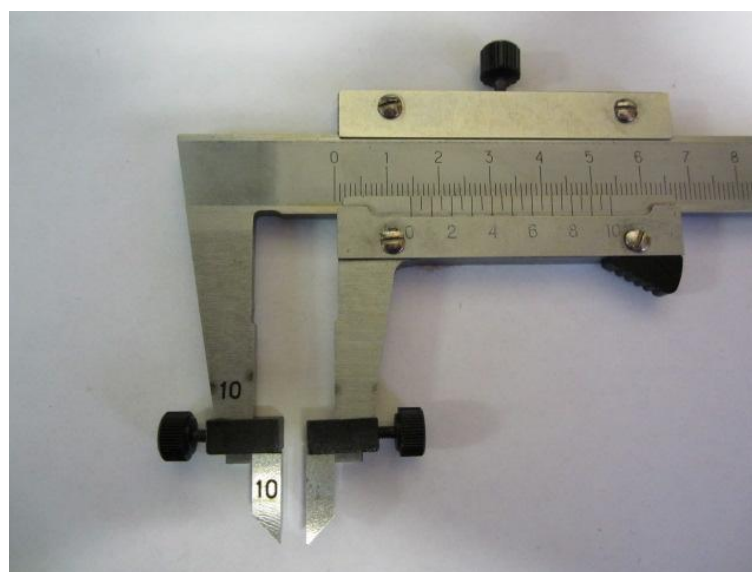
Сменные твердосплавные насадки для разметки к губкам о штангенциркуля
